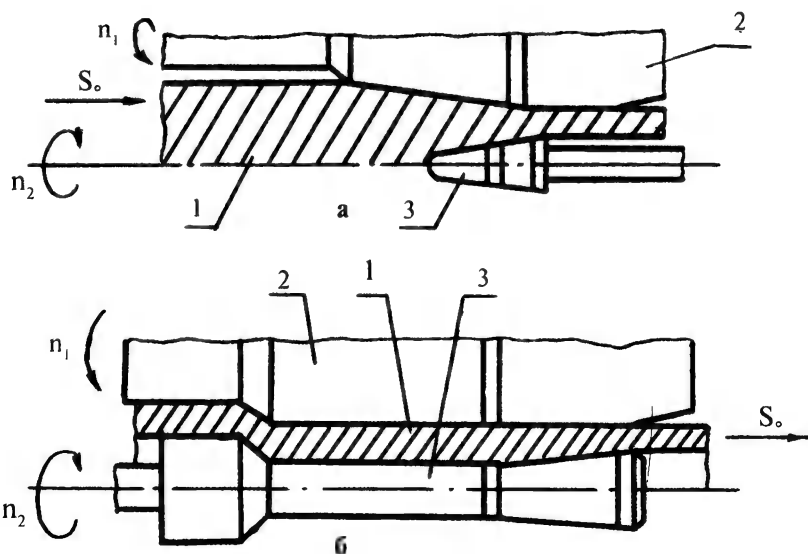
Получение трубных заготовок прошивкой на стане винтовой прокатки (а) и последующей калибровкой (б): 1 - заготовка; 2 - валок; 3 - оправка
